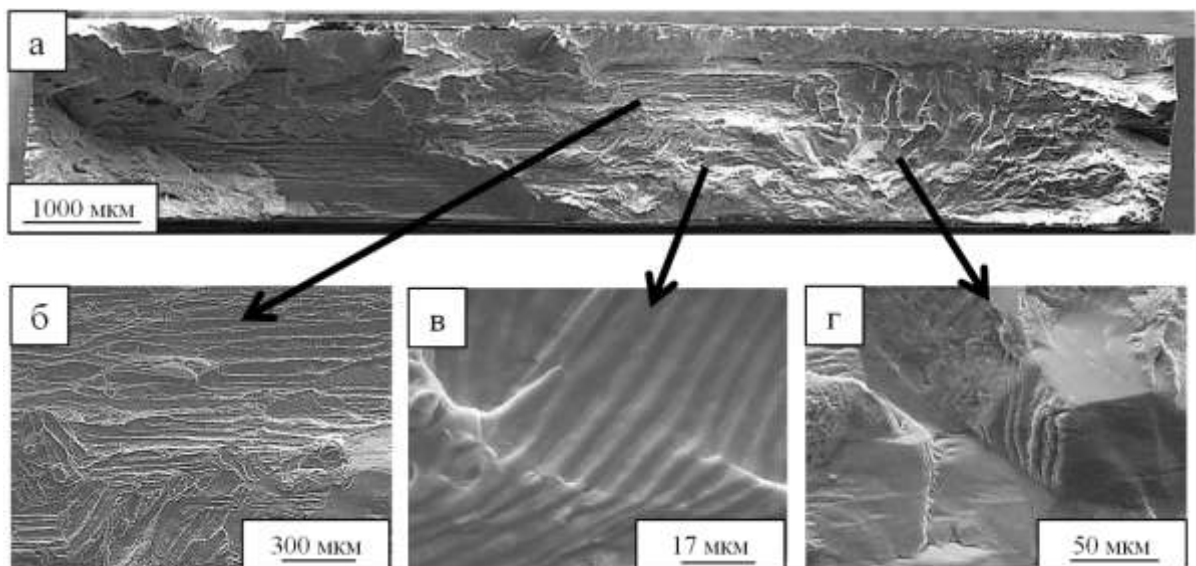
РЭМ-фрактограммы сварного соединения титанового сплава ВТ23 после МЦУ без проведения обработки. (а) панорама излома, (б) волокнисто-полосчатый рельеф с пластической вытяжкой на вершинах гребней, (в) бороздки усталостного разрушения, (г) фасетки квазискола при усталостном разрушении
